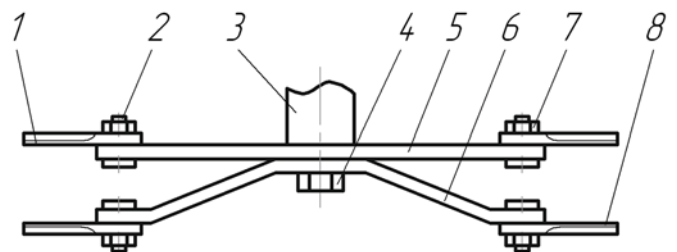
Схема двоярусного різального апарата з паралельною установкою ножів: 1 – ніж верхнього ярусу; 2 – вісь кріплення ножа; 3 – ведений вал конічного редуктора; 4 – болт; 5 – тримач верхнього ярусу; 6 – тримач нижнього ярусу; 7 – гайка; 8 – ніж нижнього ярусу
